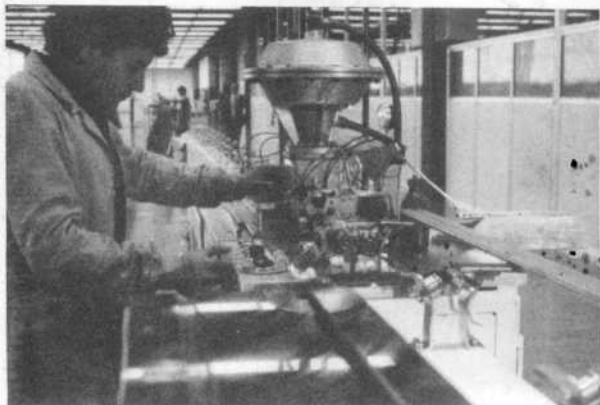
Soldadura TIG de la unión tapón-vaina.
